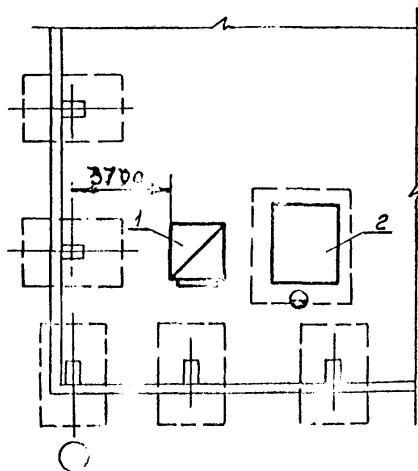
Схема распределения участка ковочных молотов с МПЧ 150-5000 кг с нагревательными камерными печами (верхнее или нижнее дымоудаление):
